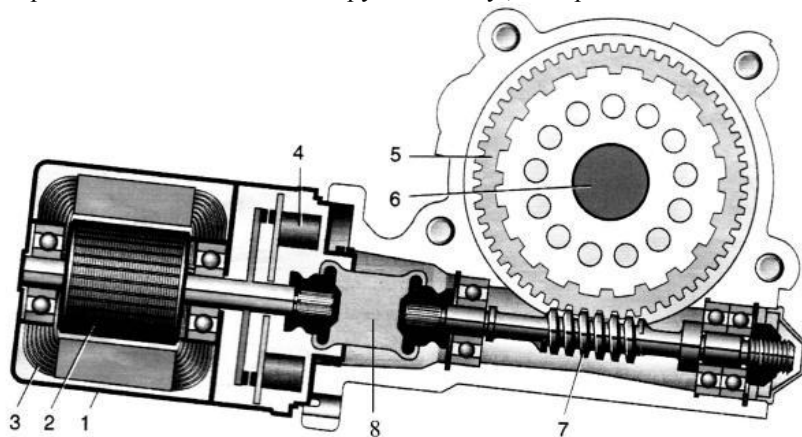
Разрез электроусилителя рулевого управления: 1 – трехфазный синхронный электродвигатель; 2 – якорь; 3 – обмотка статора; 4 – датчик положения якоря; 5 – червячное колесо; 6 – рулевой вал; 7 – червяк
